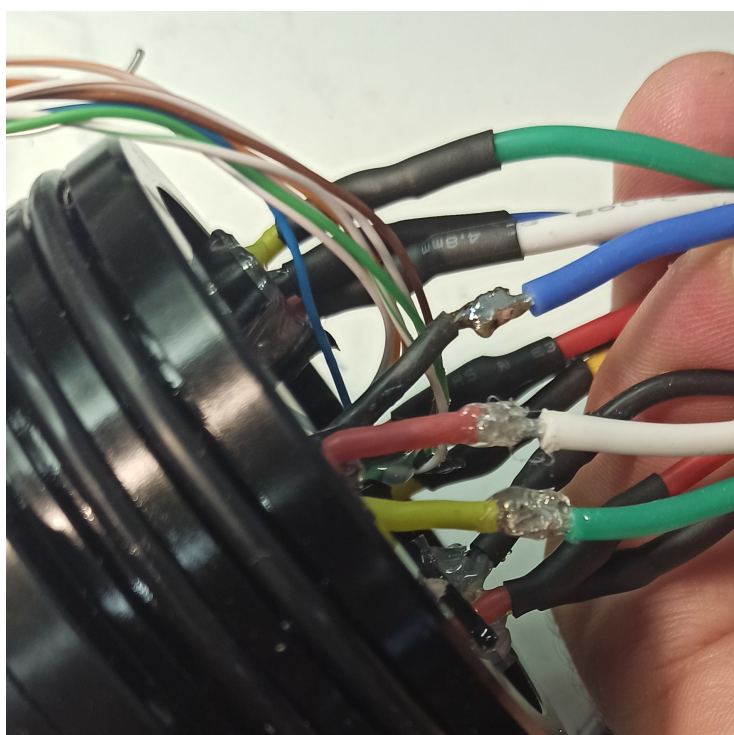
Cables d'un Basic ESC soldats a un dels motors.
